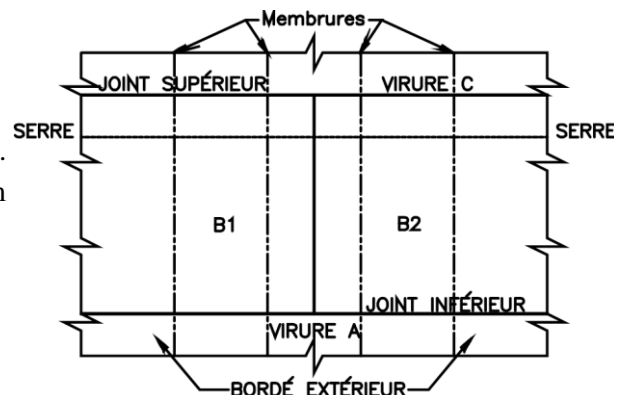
Séquence de soudage type – abouts et joints alignés
